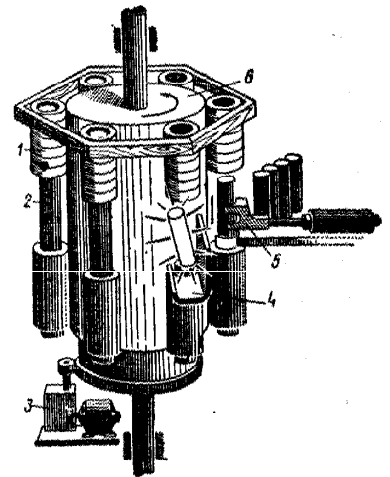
Схема карусельного нагревателя с шестью периодическими индукторами:
